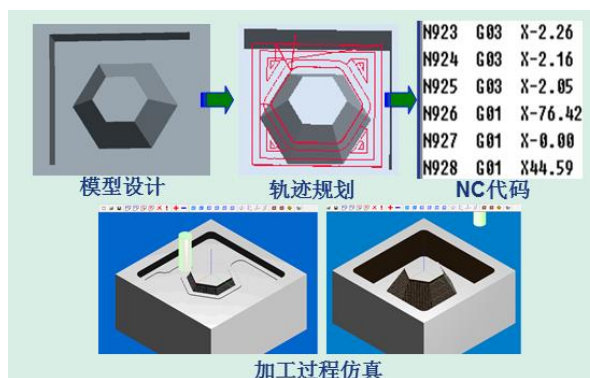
3D-SMEDM 的 CAD/CAM 过程
